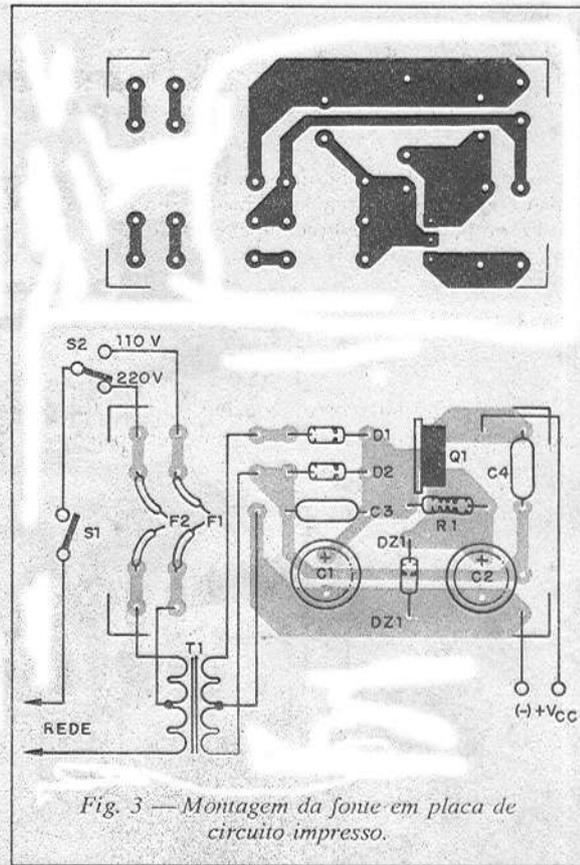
Montagem da fonte em placa de circuito impresso.
